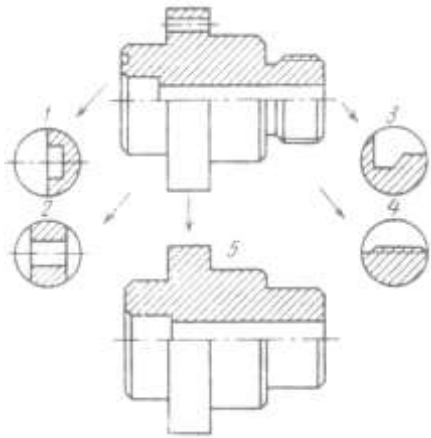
Конструктивные элементы детали: 1 – торцовая канавка; 2 – группа отверстий во фланце; 3 – резьбовая канавка; 4 – резьба; 5 – элемент основной формы [5]
